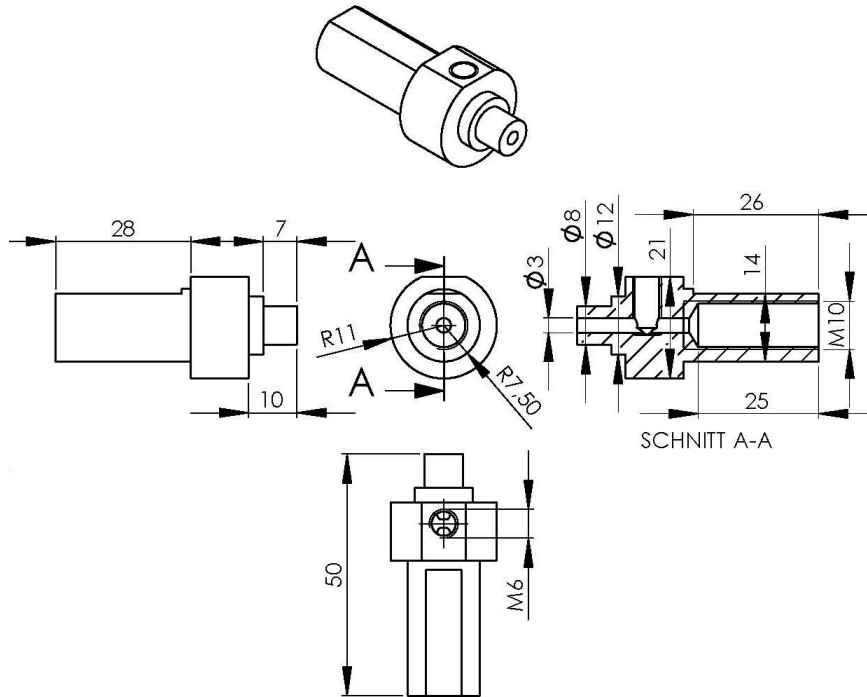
Technische Zeichnung der Werkzeugschulter Werkzeug 1
